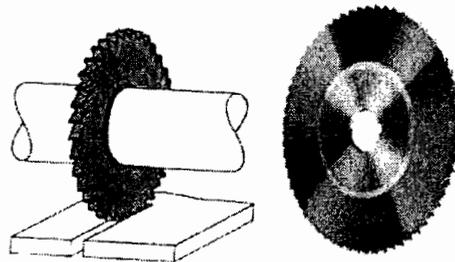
Staggered-Tooth Side-Milling Cutter เป็นดอกกัดที่มีคมตัดด้านข้างทั้งสองข้าง แต่ฟันสลับไปมา
